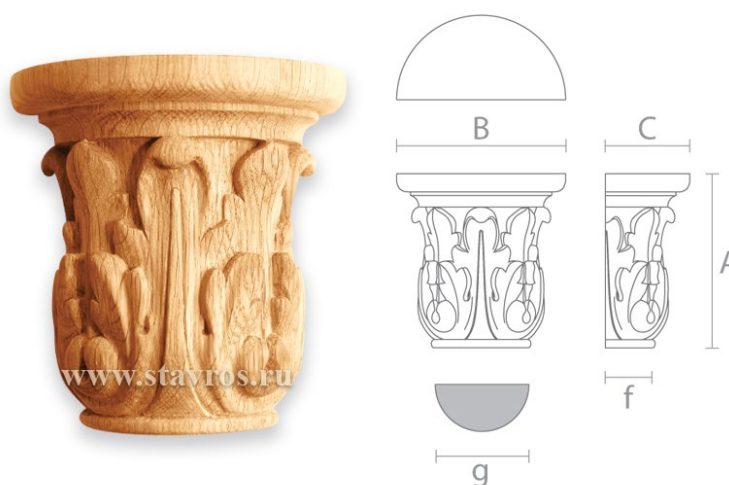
Деталь, произведенная на фрезерном станке с ЧПУ по векторной модели
